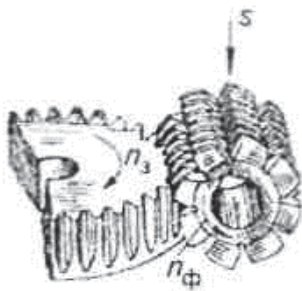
Схема нарезания зубьев колеса червячной фрезой
